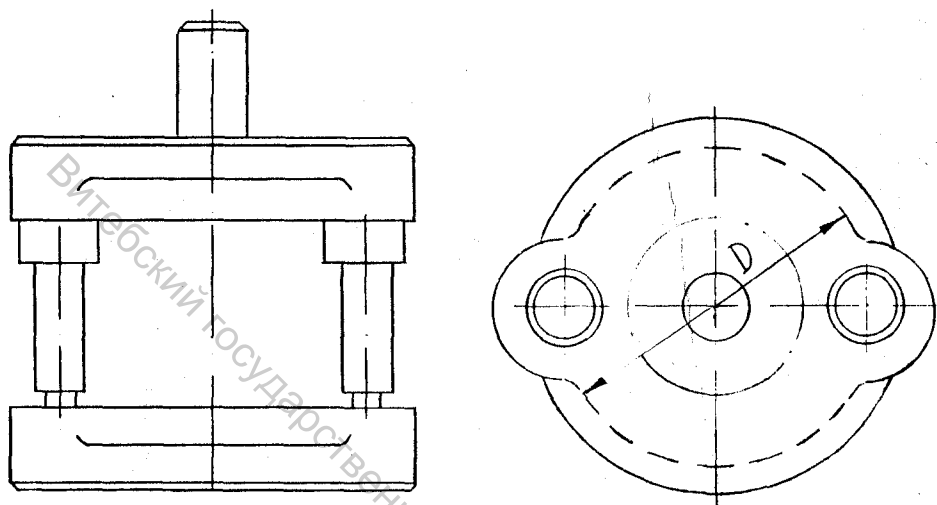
Рис. I.II. Круглый стандартный блок с осевым расположением направляющих колонок.
